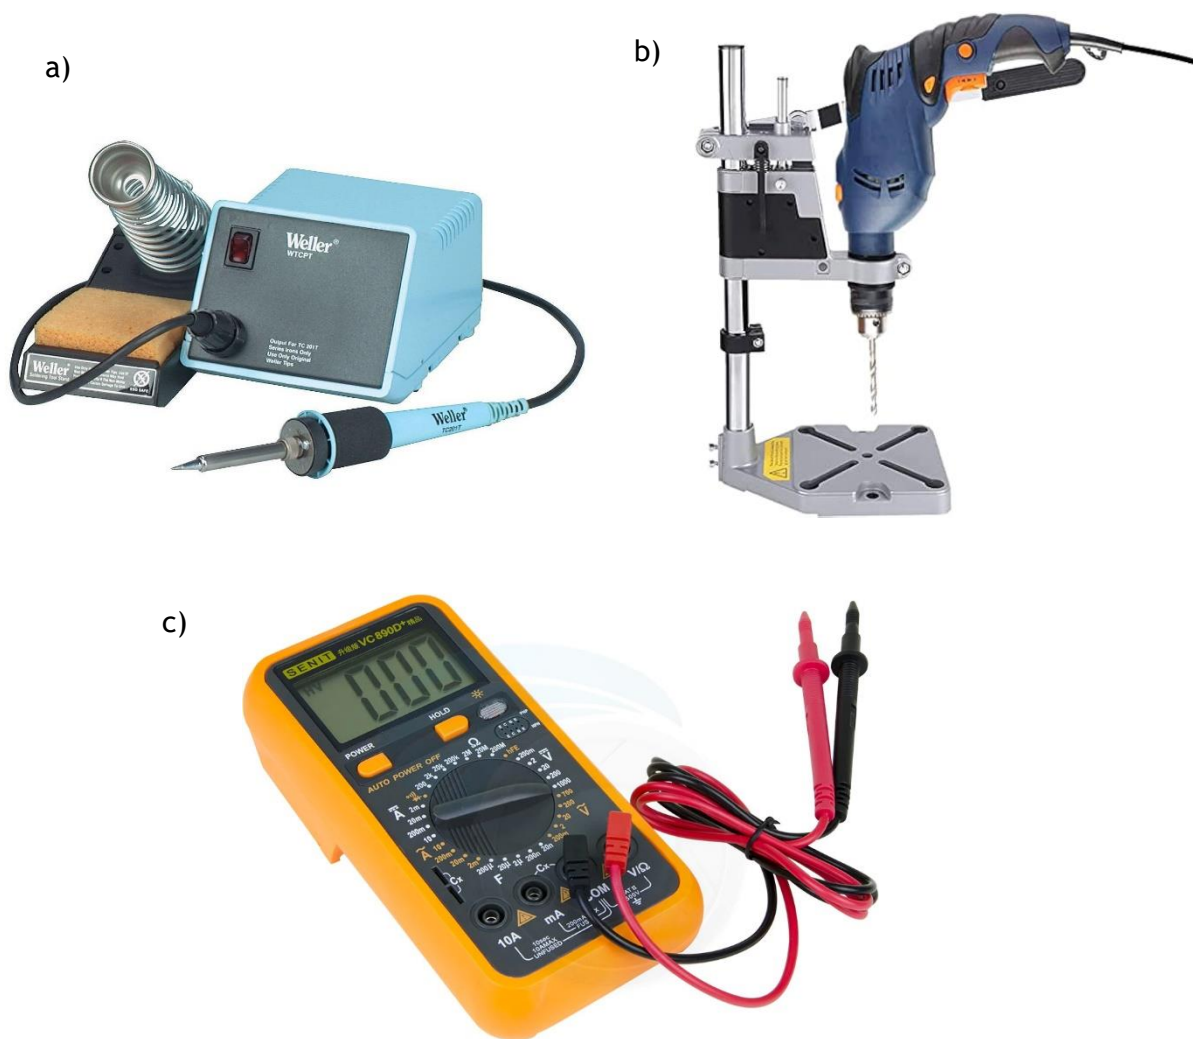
Herramientas utilizadas para hacer la soldadura de los componentes en la placa. a) Herramienta de soldaduras; b) Taladradora con soporte para mesa; c) Multímetro.¹⁸
